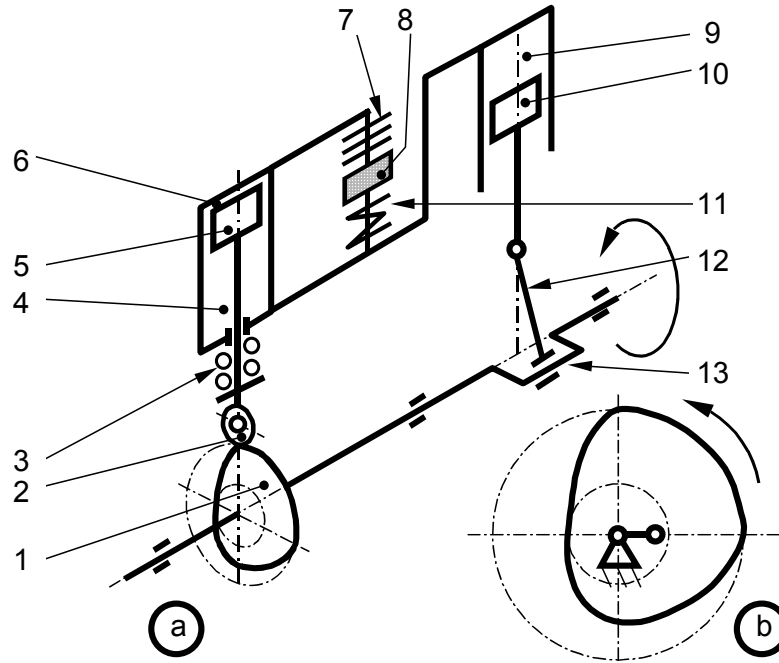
Motor Stirling de tip „gama“ cu mecanism cu camă:
